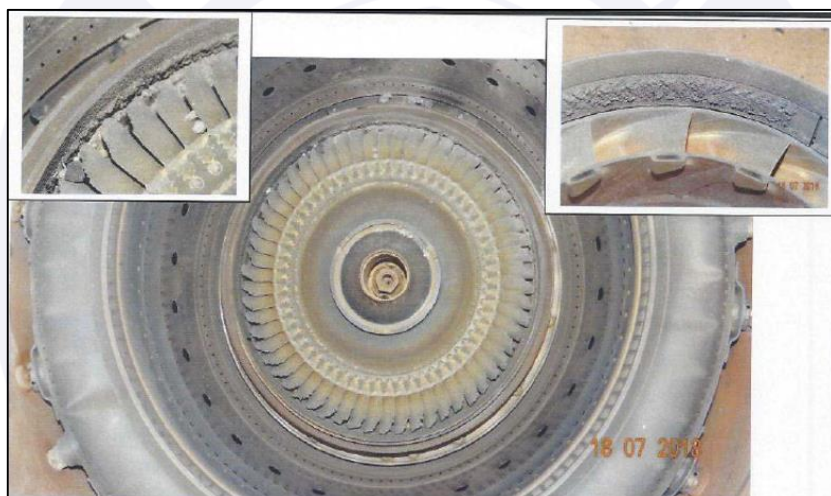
Imagens do motor mostrando o rotor da turbina do compressor com as palhetas derretidas. Os destaques mostram o material das palhetas depositado sobre o anel segmentado.
